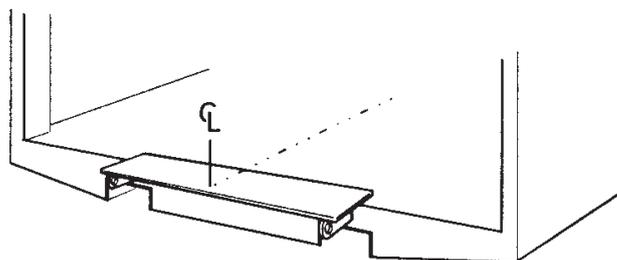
Atornillar o soldar el accesorio de montaje en la barra trasera No. ref. 51724TL para Z 10/15/20
